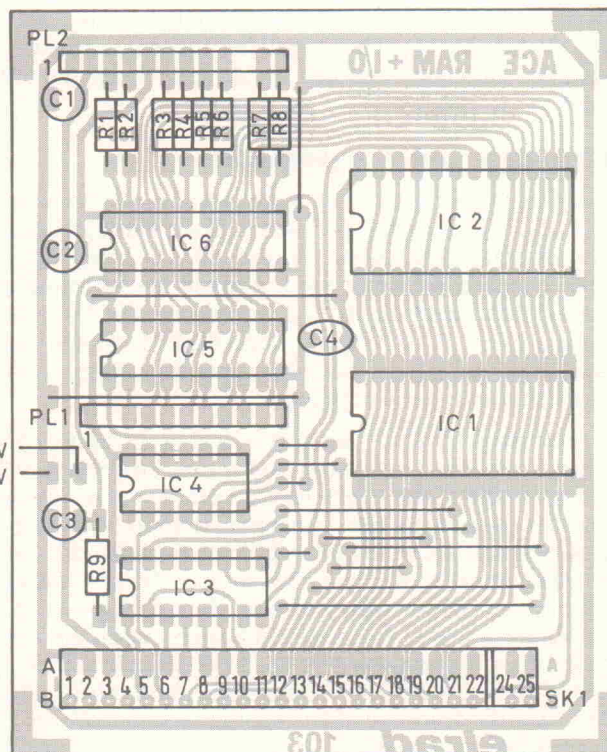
Platinenlayout mit Bestückungsplan. Drahtbrücken sind notwendig, um eine einseitige Platine zu erhalten.
